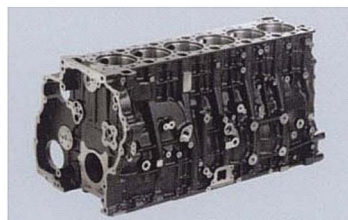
Блок цилиндров двигателя R6 (масса 362 кг)
